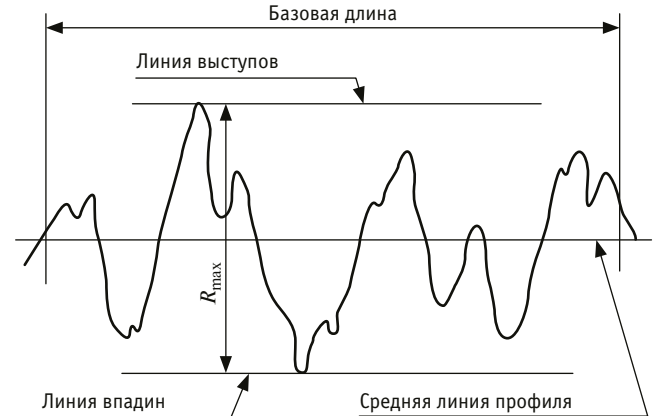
Микрорельеф шероховатости поверхности головки рельса и поверхности катания колеса
